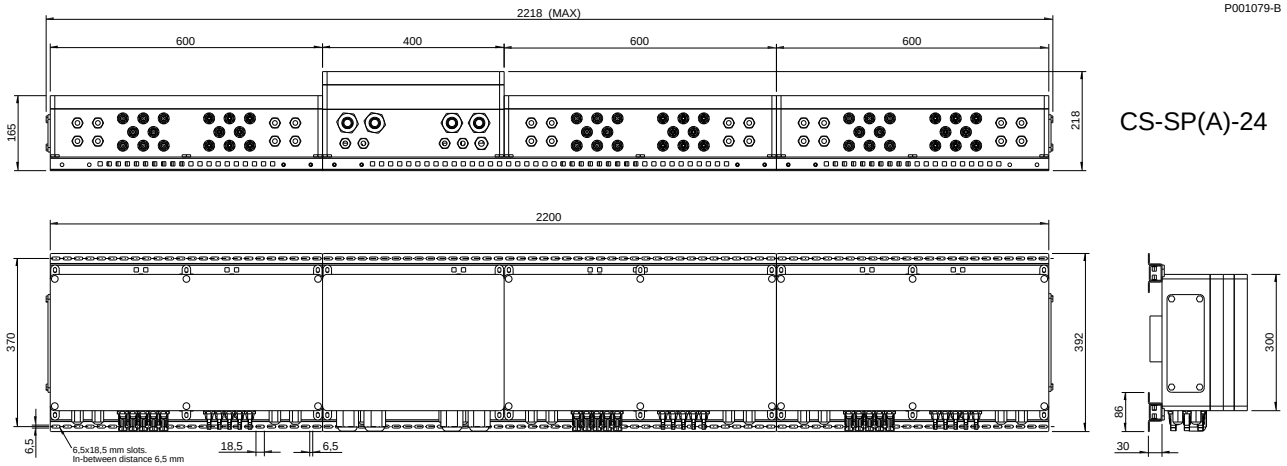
Размеры коммуникатора SMART STRING BOX.
